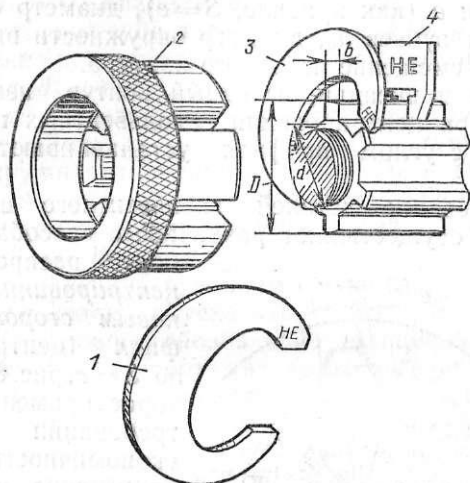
Калибры для контроля шлицевого прямобочного вала:
